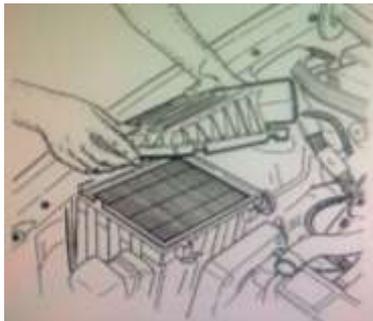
Desmontaje de Tapa del Filtro de Aire
